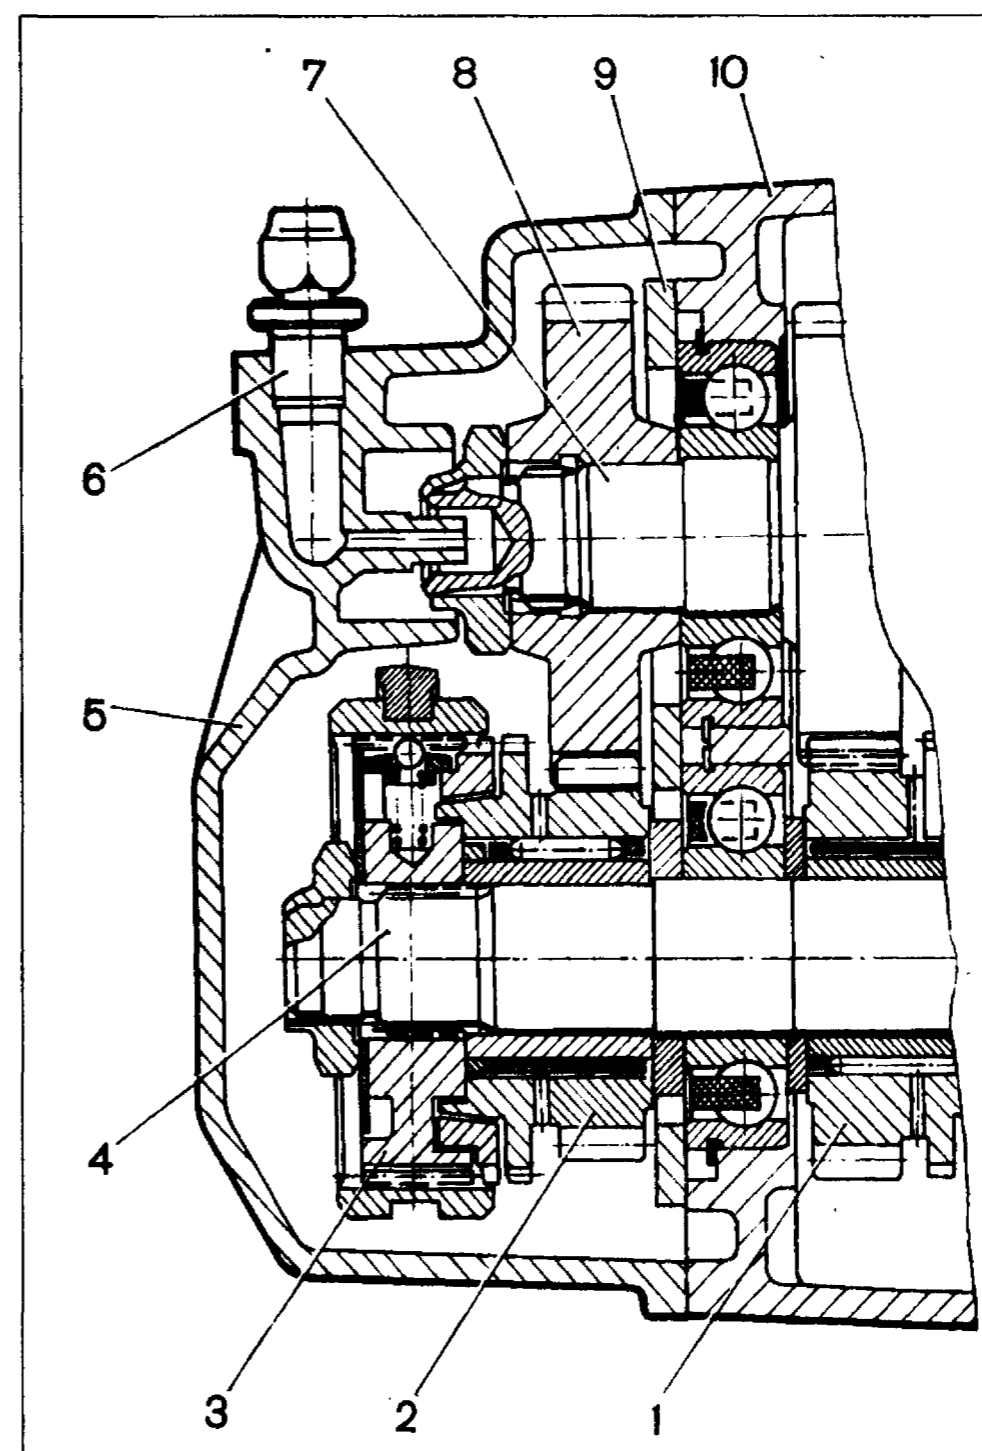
Задняя часть пятиступенчатой коробки передач: 1 — ведомая шестерня IV передачи вторичного вала; 2 — ведомая шестерня V передачи вторичного вала; 3 — синхронизатор V передачи; 4 — вторичный вал; 5 — задняя крышка картера коробки передач; 6 — сапун; 7 — первичный вал; 8 — ведущая шестерня V передачи; 9 — упорная пластина крепления подшипников; 10 — картер коробки передач
